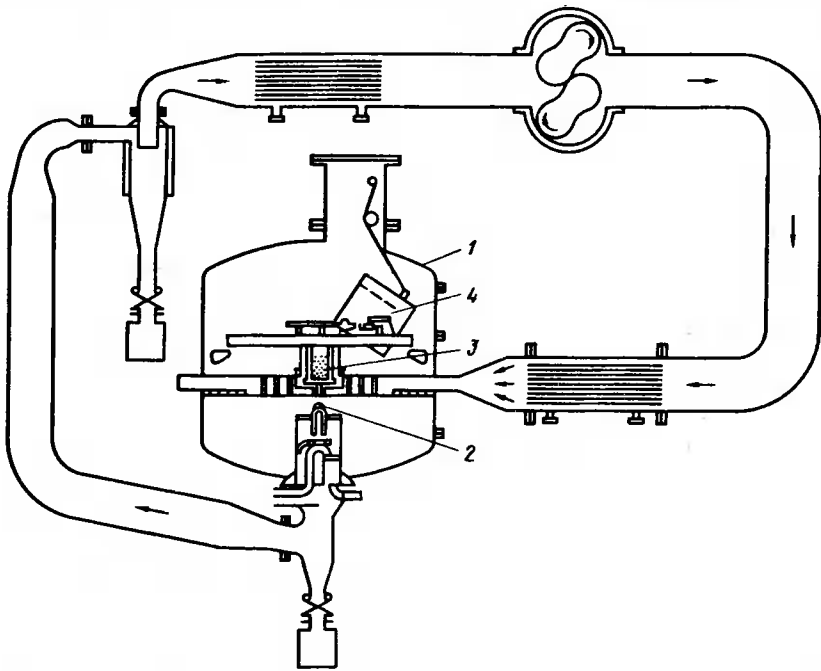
Установка центробежного распыления расплава в гелии [65]
